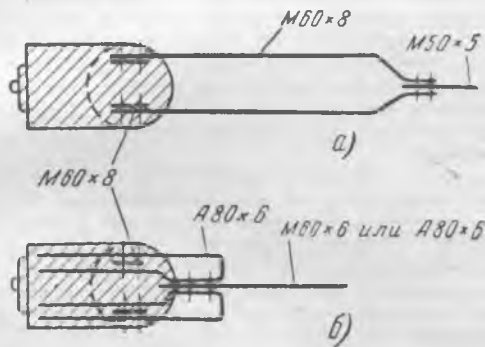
Теплоотвод выключателя ВМГ-133 1 000 а (вид снизу на корпус выключателя). а — существующая конструкция; б — предлагаемая конструкция.
